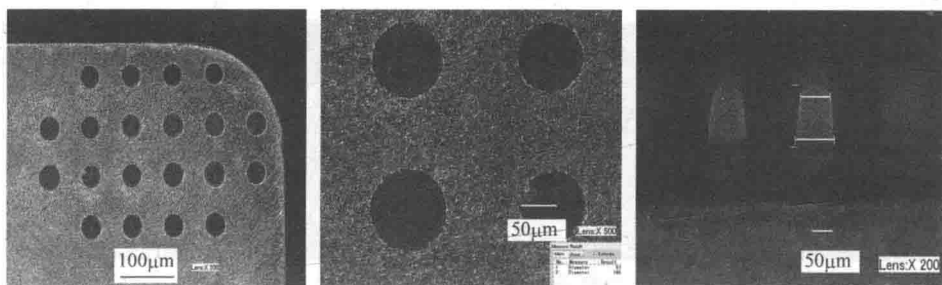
硬质合金刀具表面微细电火花加工的微结构形貌
